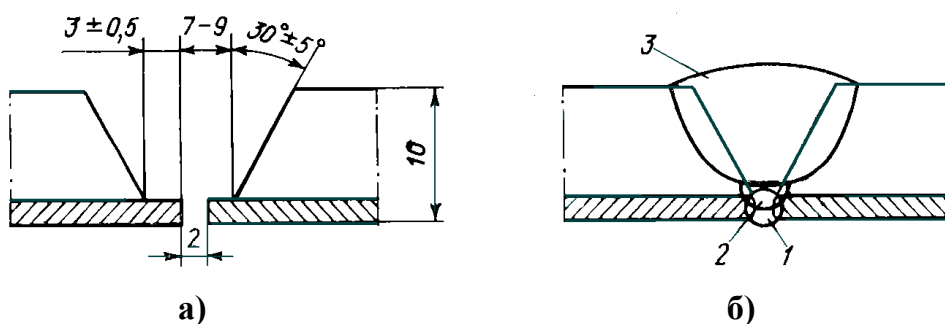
Разделка кромок (а) и нанесение сварочных слоев (б) при сварке двухслойных сталей
